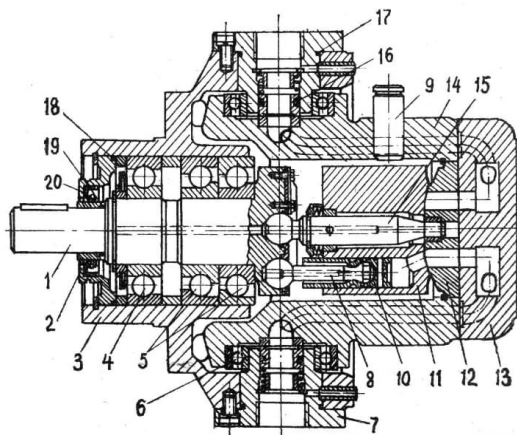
Сдвоенный аксиально-поршневой насос серии 207: 1 – вал приводной; 2 – крышка передняя; 3 – корпус неподвижный; 4, 5, 6 – подшипники; 7 – подводный фланец; 8 – шатун; 9 – цапфа; 10 – поршень; 11 – блок цилиндров; 12 – диск распределительный; 13 – крышка задняя; 14 – корпус подвижный; 15 – шип; 16, 17 – уплотнения
